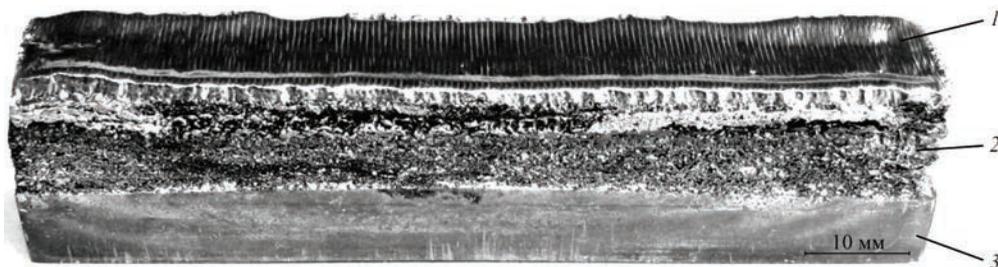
Образец, изготовленный методом электронно-лучевой 3D-наплавки: 1 — верхний слой наплавленного металла; 2 — промежуточный слой металла с частицами нерасплавленного порошка по бокам образца; 3 — подложка из титана
